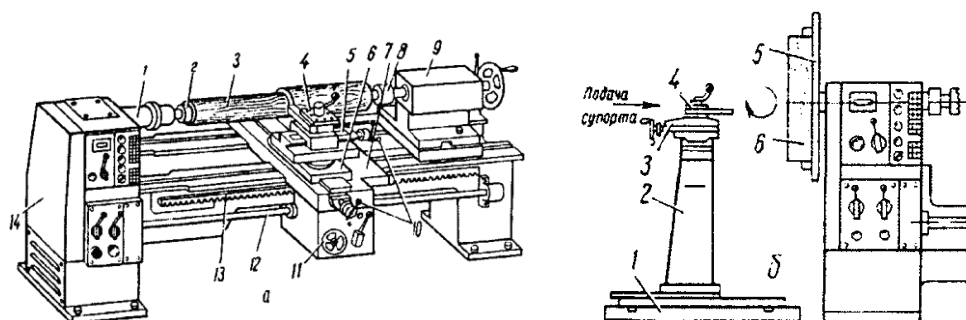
Загальний вигляд токарного верстата з механізованою подачею і приставним лобовим пристроєм: а – загальний вигляд: 1 – шпиндель; 2 – передній центр; 3 – заготівка; 4 – держак; 5 – поздовжній супорт; 6 – поперечний супорт; 7 – механізований поздовжній супорт; 8 – центр; 9 – задня бабка; 10, 11 – маховички; 12 – вал; 13 – зубчаста рейка; 14 – тумба; б – приставний пристрій з планшайбою: 1 – основа; 2 – стояк; 3 – супорт; 4 – тримач для різця; 5 – планшайба; 6 – заготівка
